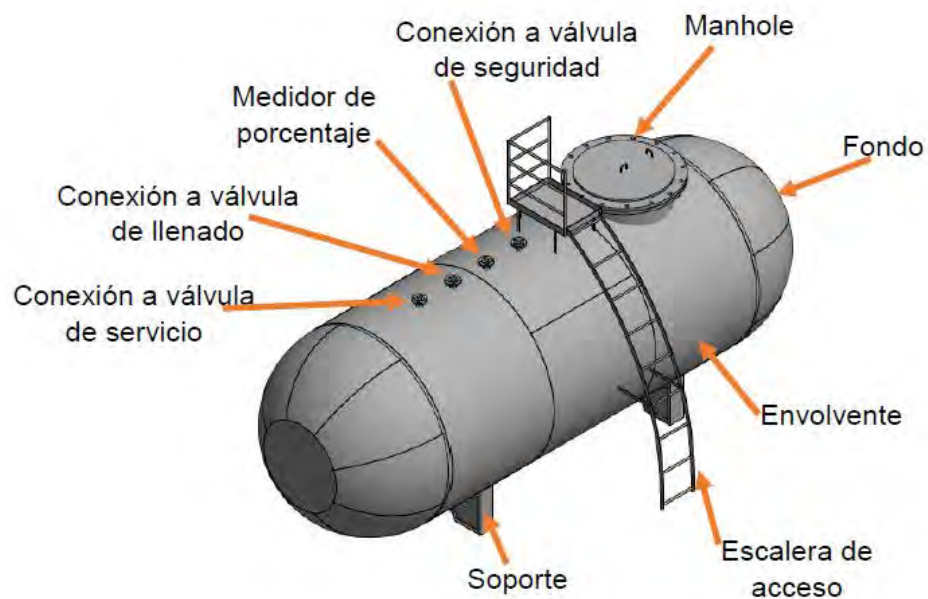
Vista isométrica de tanque de almacenamiento de GLP
